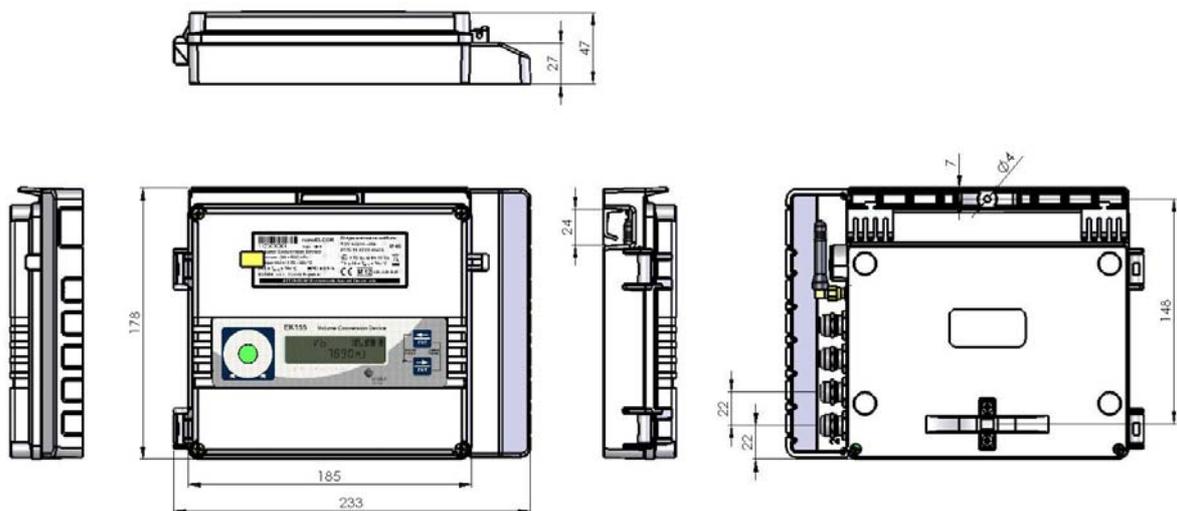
Dimensioni del dispositivo (con copertura cavi)
